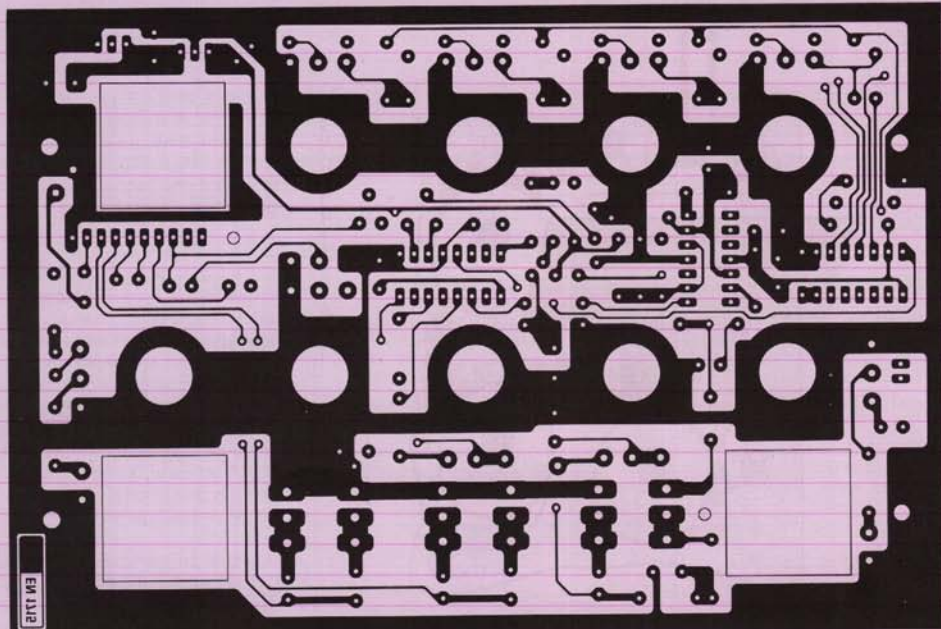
1 : Dessin, à l'échelle 1, du circuit imprimé double face à trous métallisés de la platine du distorseur pour guitare et basse, face soudures.
